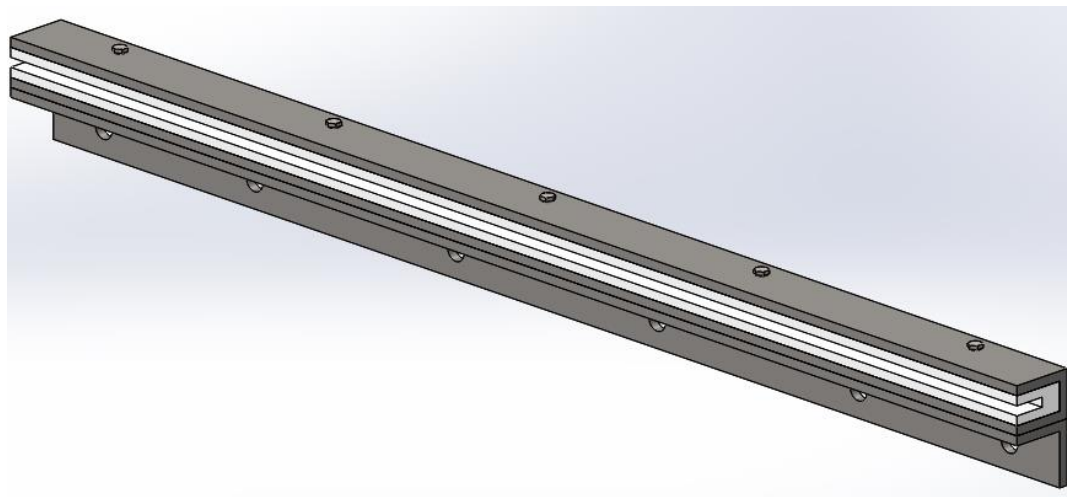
Conjunto das calhas com a estrutura de suporte
